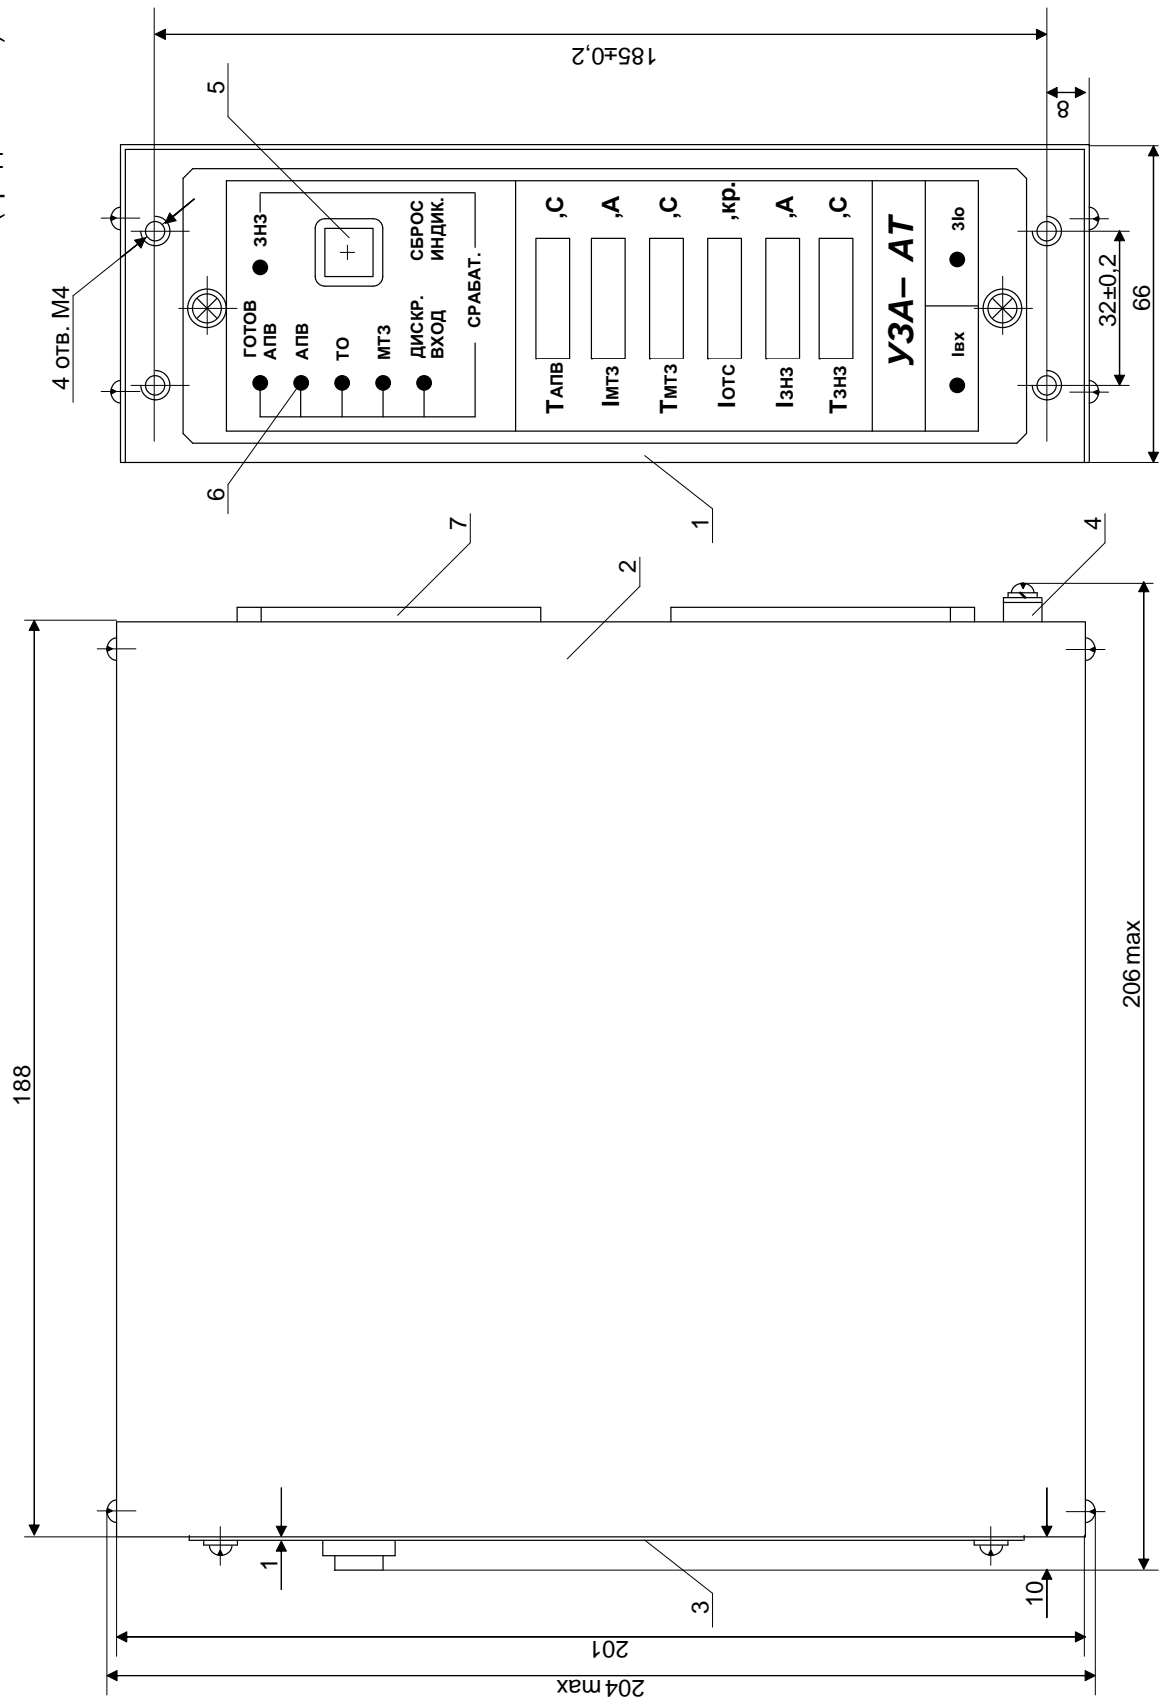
Внешний вид, габаритные и установочные размеры УЗА-АТ (крепление на широкой стороне)
